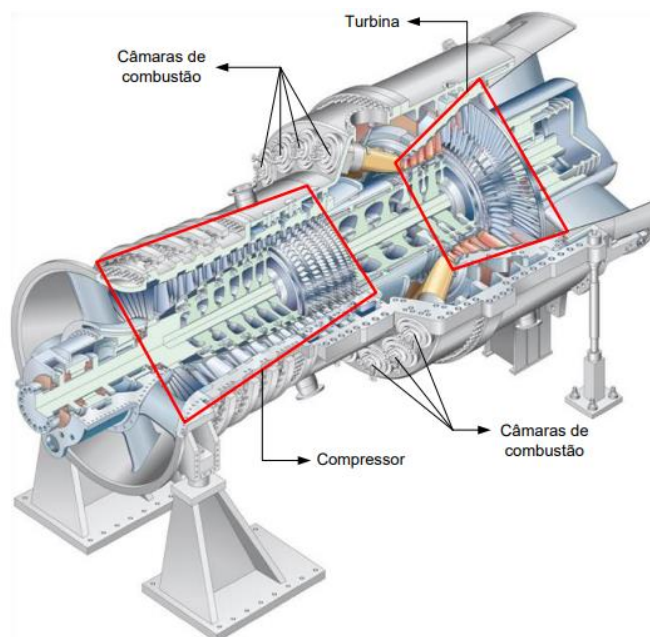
Principais seções da turbina a gás SGT5 - 4005. Fonte: Siemens.
